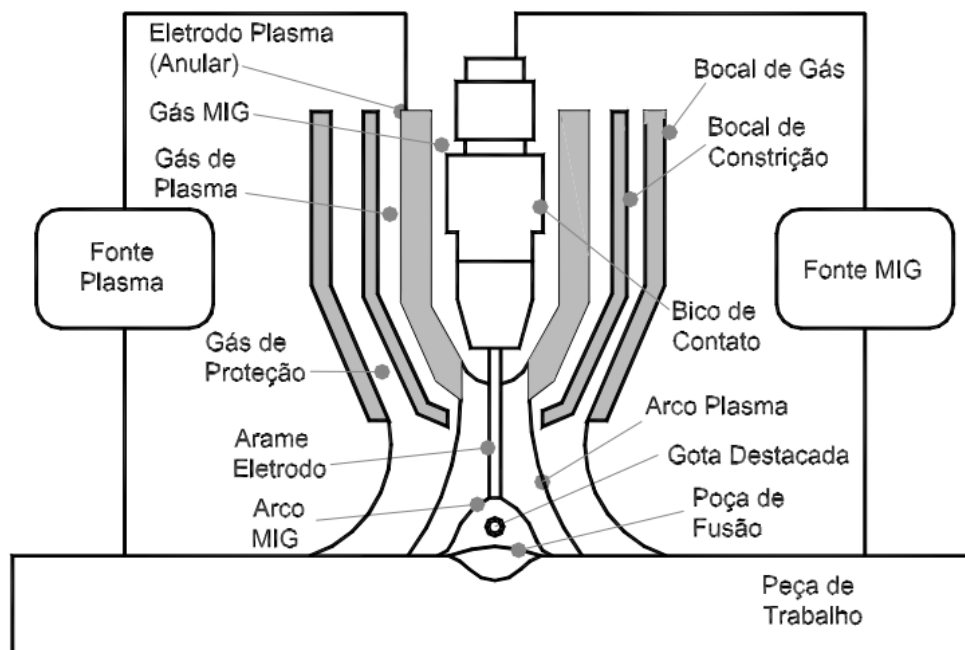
Esquema da tocha de soldagem no caso do processo Plasma-GMAW Coaxial [29].
